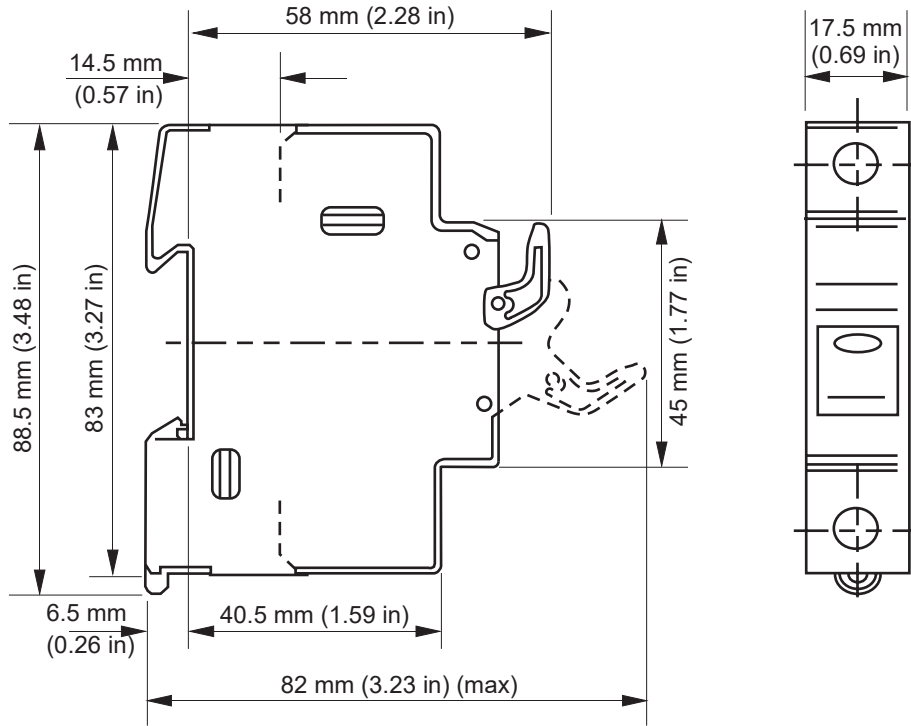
Las dimensiones del portafusibles: US101 (10x38 mm)
